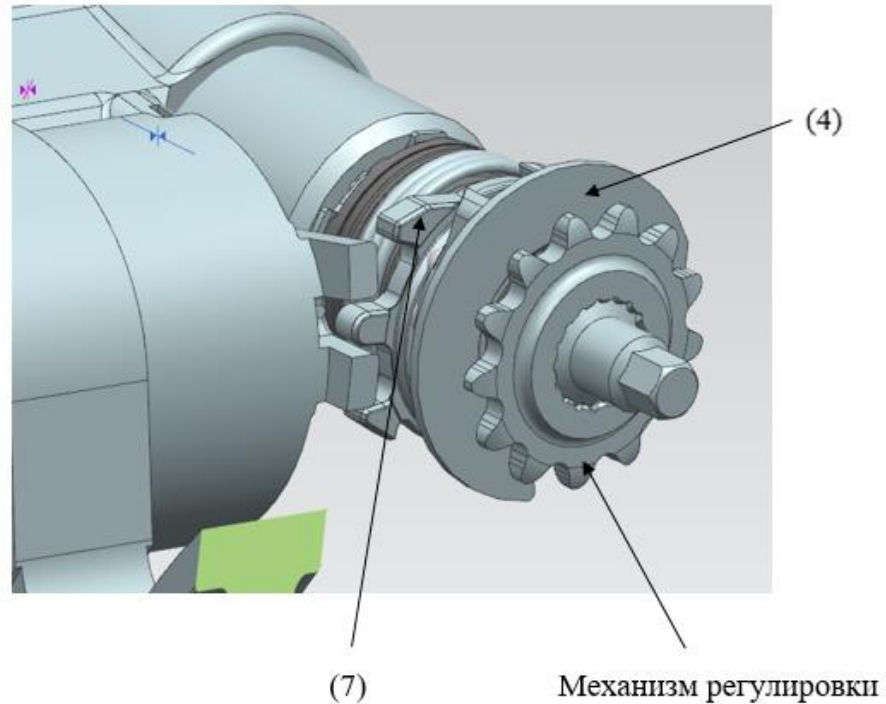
Увеличенный вид контакта механизма регулировки и рычага
